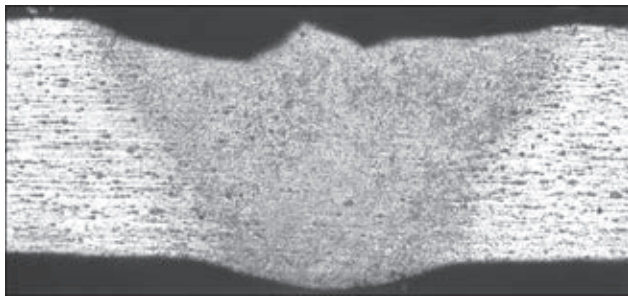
Макроструктура ($\times 25$) поперечного сечения стыкового сварного соединения сплава АМг6 ($\delta = 1,4$ мм), выполненного плазменным способом со скоростью сварки 30 м/ч
